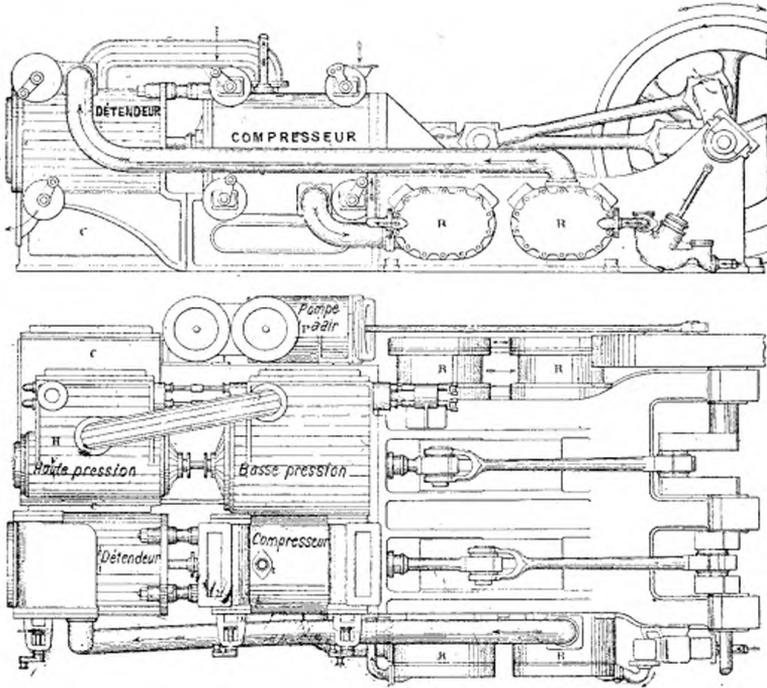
et 54. — *Lightfoot*. Machine horizontale à moteur compound RR refroidisseur, C condenseur à surfaces.
